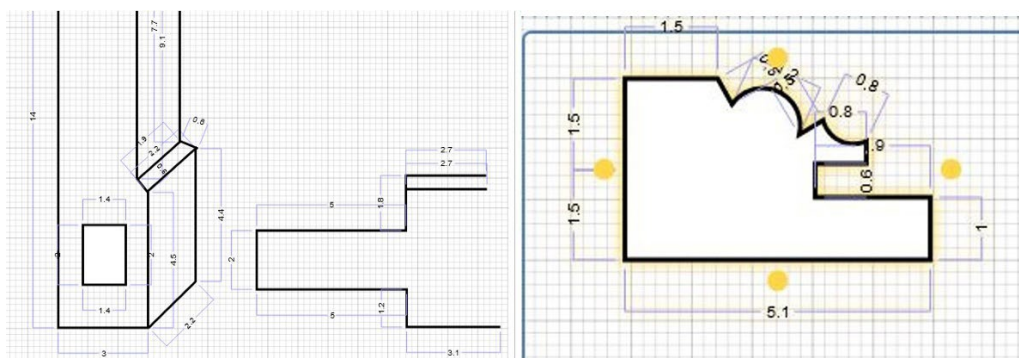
Planimetría de estructura del marco. Aut.: Alejandra del Barrio Luna.
